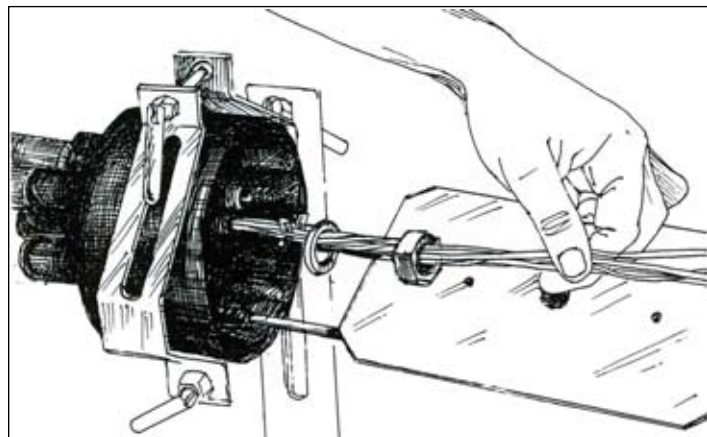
Установка на ОК деталей шайбы и гайки штуцера
